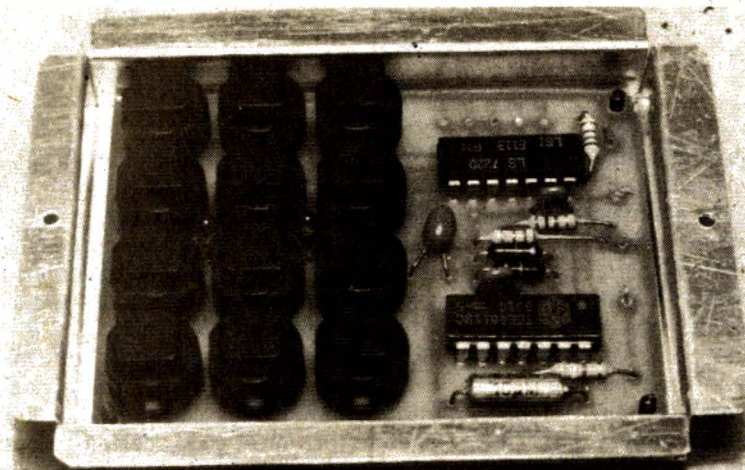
Photo A. - Le module de commande. Les composants sont soudés le plus à plat possible de manière à ne pas dépasser la hauteur intérieure des touches. Noter la manière de réaliser la partie arrière du boîtier. Alu de 5/10.
